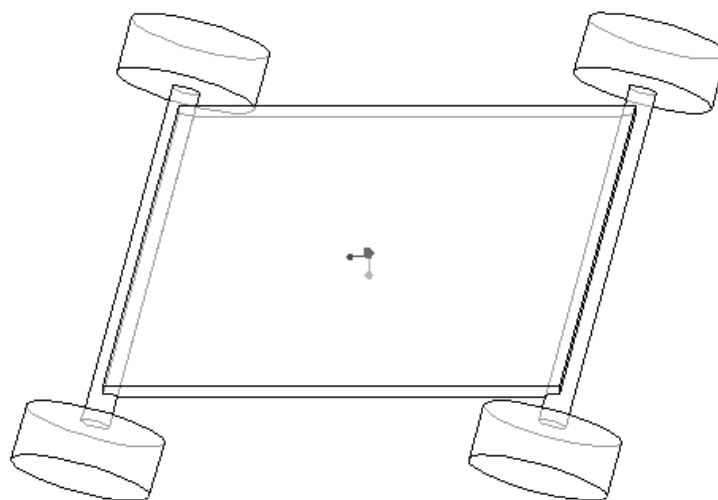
Prikaz vertikalnog savijanja konstrukcije [3]
